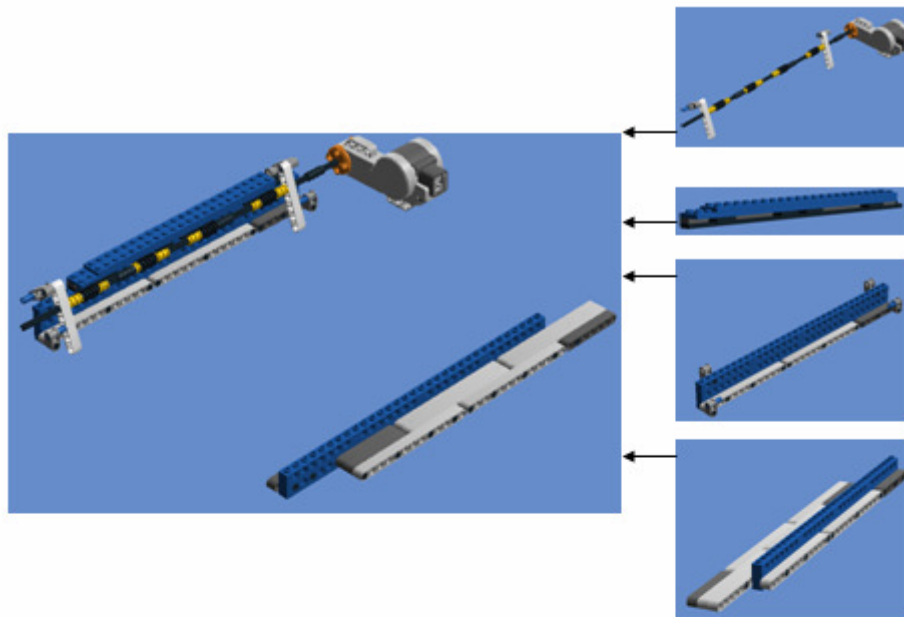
B.B1.3 ): Piezas para el montaje de los pilares y los mandos de control.
